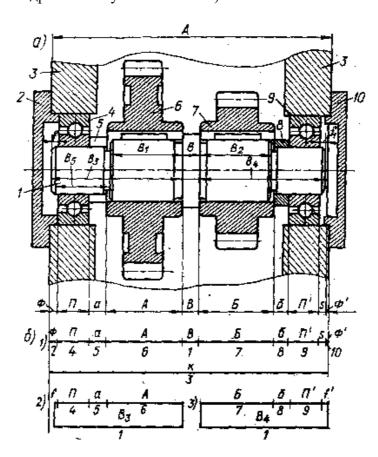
Сборочный чертёж узла (a) со сборочными цепями
